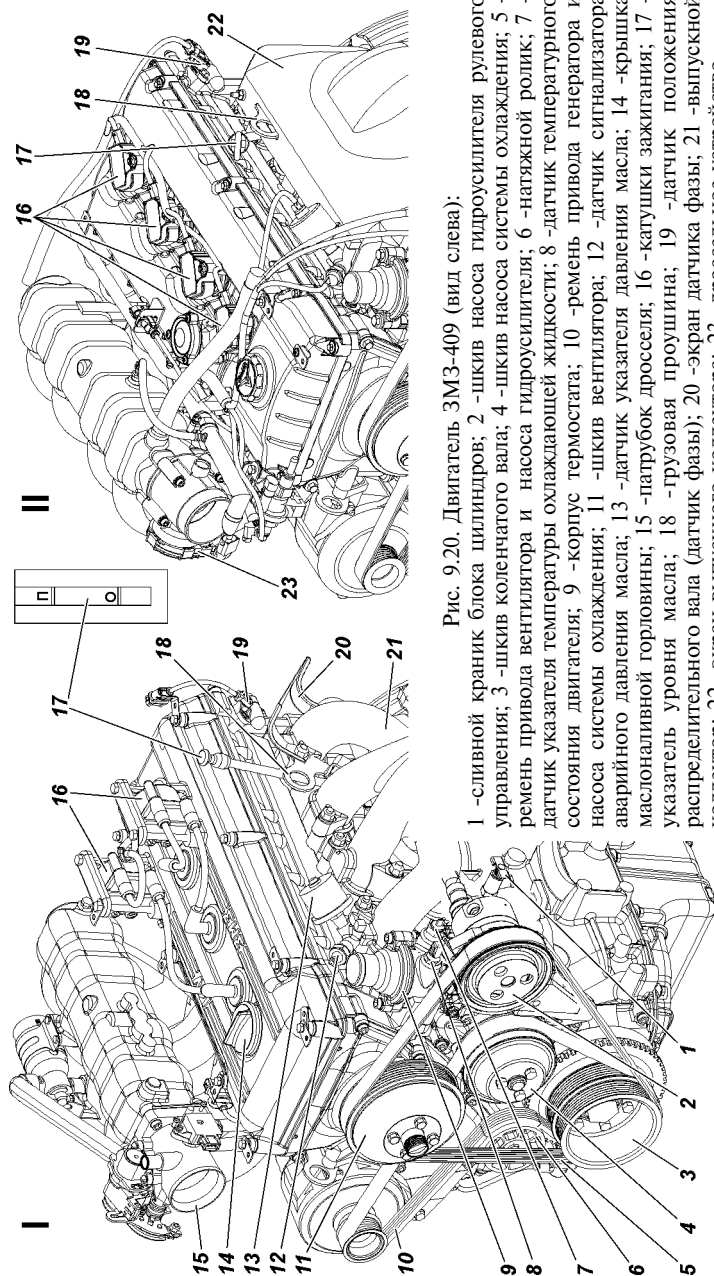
Двигатель 3МЗ-409 (вид слева):
